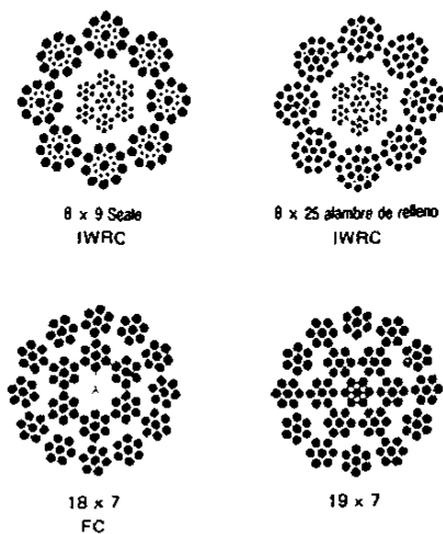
Secciones transversales de algunos cables metálicos resistentes a la rotación.
